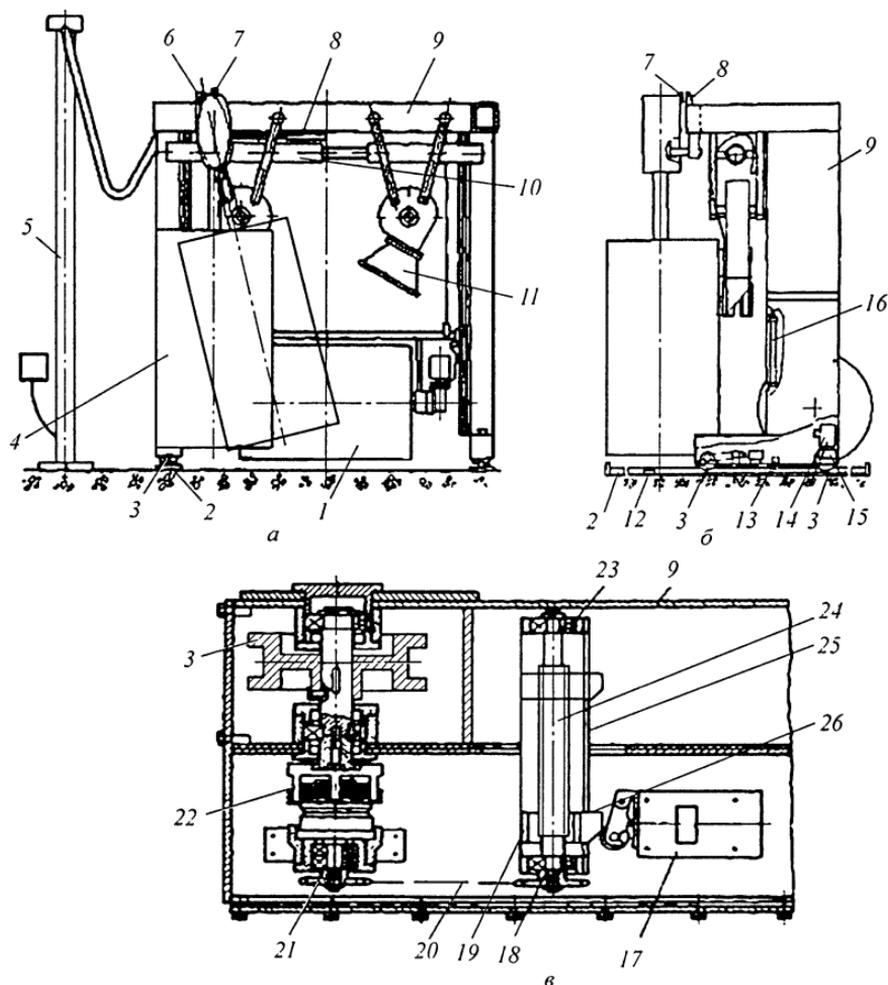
Щеточная моечная установка с устройством для сушки (обдува) автомобиля: *а* — общий вид; *б* — устройство вертикальной щетки; *в* — устройство перемещения установки; 1 — горизонтальная щетка; 2 — рельс; 3 — опорный ролик; 4 — вертикальная щетка 5 — стойка; 6 — бесконтактный датчик; 7 — пластина; 8, 10 и 16 — пневмоцилиндры; 9 — рама; 11 — вентиляторы; 12 и 17 — конечные выключатели; 13 — упор; 14 — электродвигатель; 15 — редуктор; 18 и 21 — звездочки; 19 — гайка; 20 — цепная передача; 22 — электромагнитная муфта; 24 — ходовой винт; 25 — направляющие; 26 — упор
